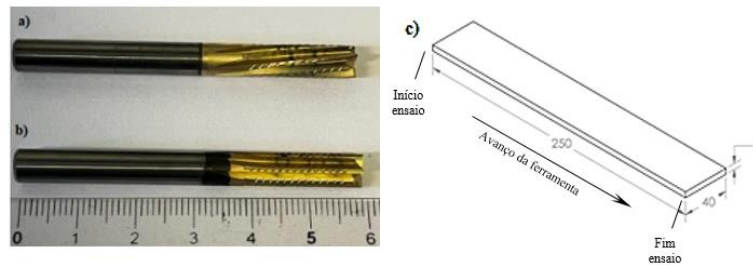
Ferramentas de corte ensaios de fresamento. a) Fresa hélice à esquerda (HE); b) Fresa hélice neutra (HN); c) Corpo de prova compósito e detalhamento do fresamento (Autoria Própria)
